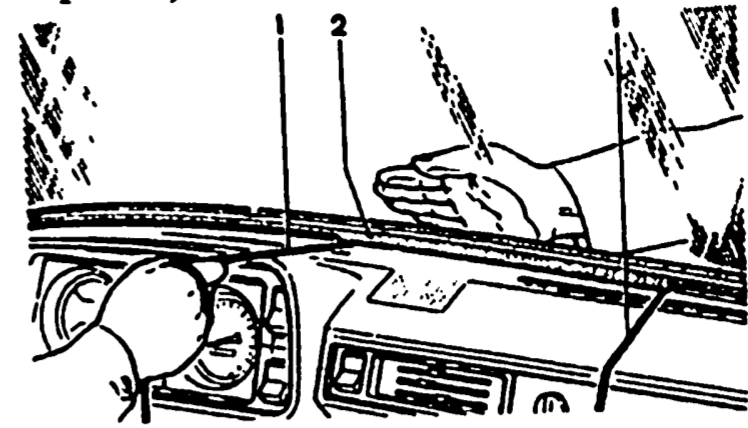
Установка ветрового стекла: 1 - шнур для установки стекла; 2 - уплотнитель
